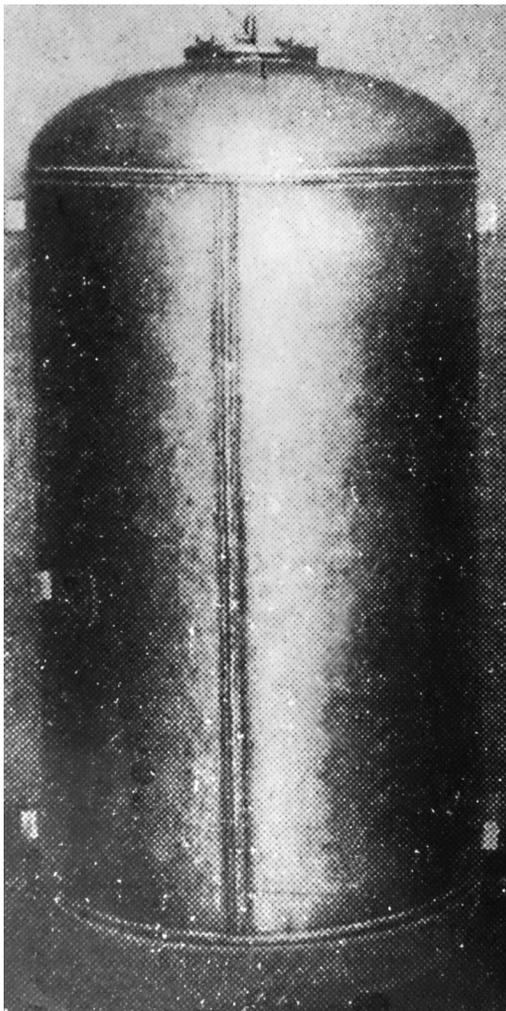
Внешний вид резервуара из технического титана, выполненного автоматической сваркой под слоем флюса АНТ-Т1
